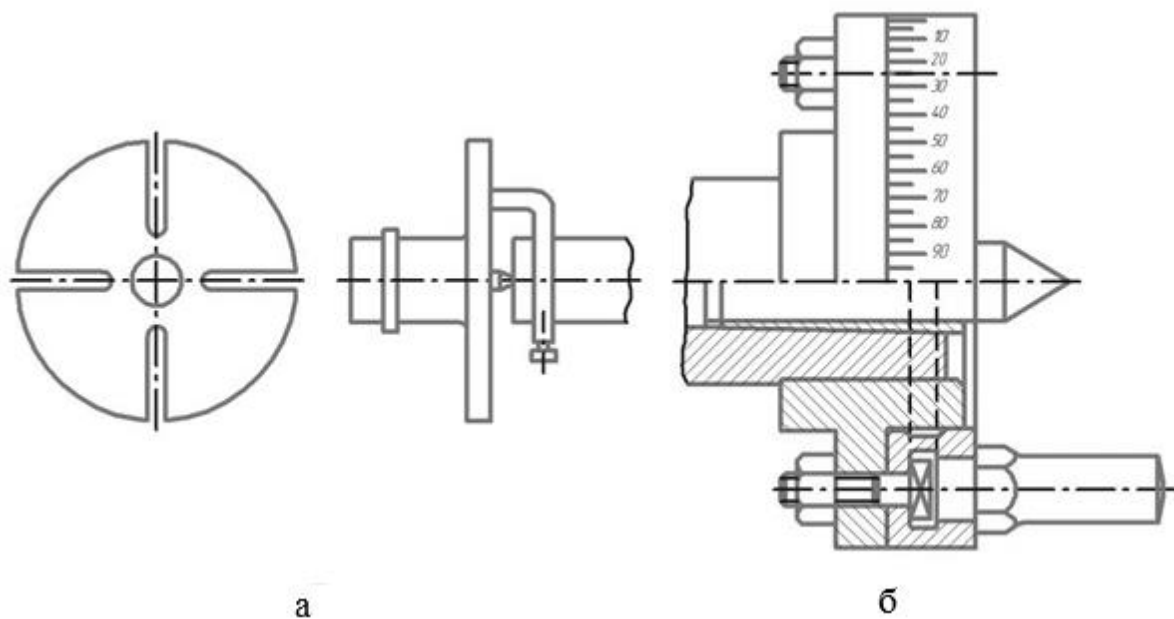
Повідкові патрони для нарізування багатозахідних різьб
